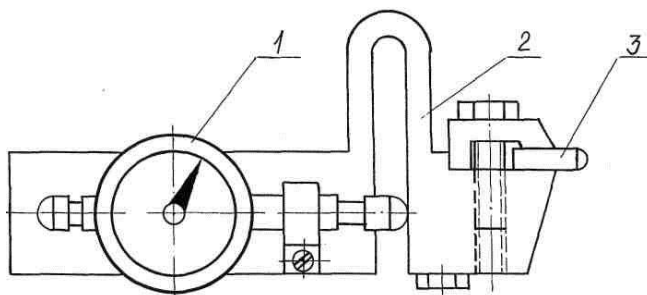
Державка для крепления высаживающих и сглаживающих пластин: 1 — индикатор для установки усилия высаживания и сглаживания; 2 — державка; 3— рабочая пластина твердого сплава.
